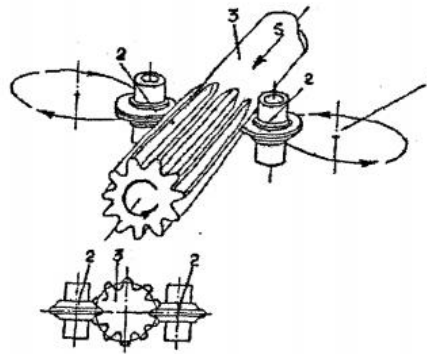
Схема ППД зубчатых колес профильными роликами
